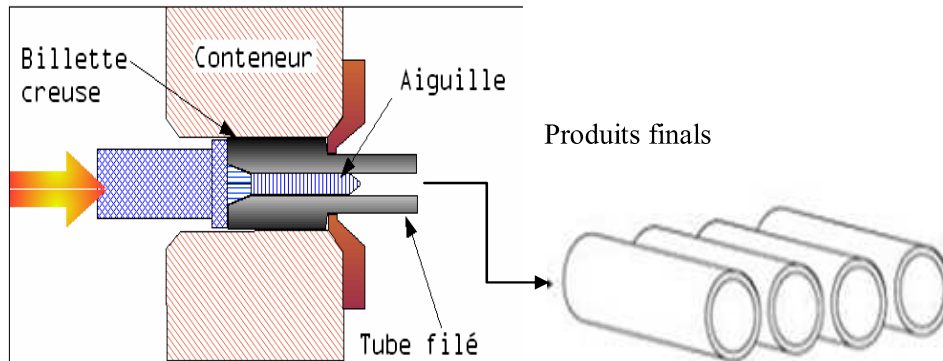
Fabrication de pipe sans soudure « Schéma du filage sur aiguille permettant d'obtenir un tube sans soudure ».
